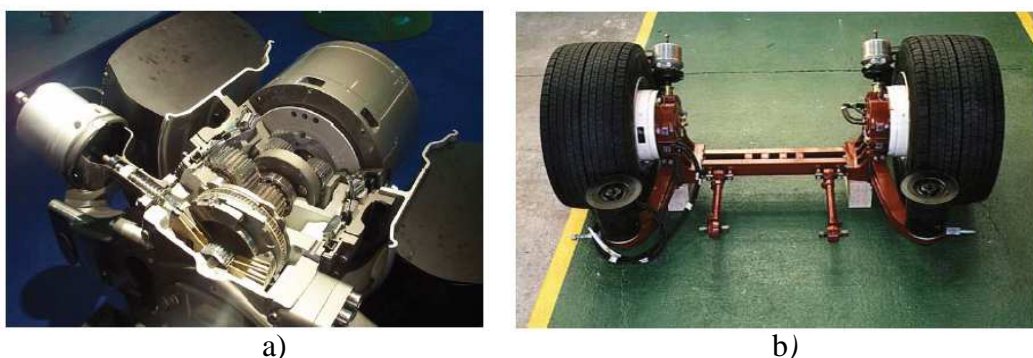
a) Pormenor de motor elétrico de tração instalado num cubo de roda
